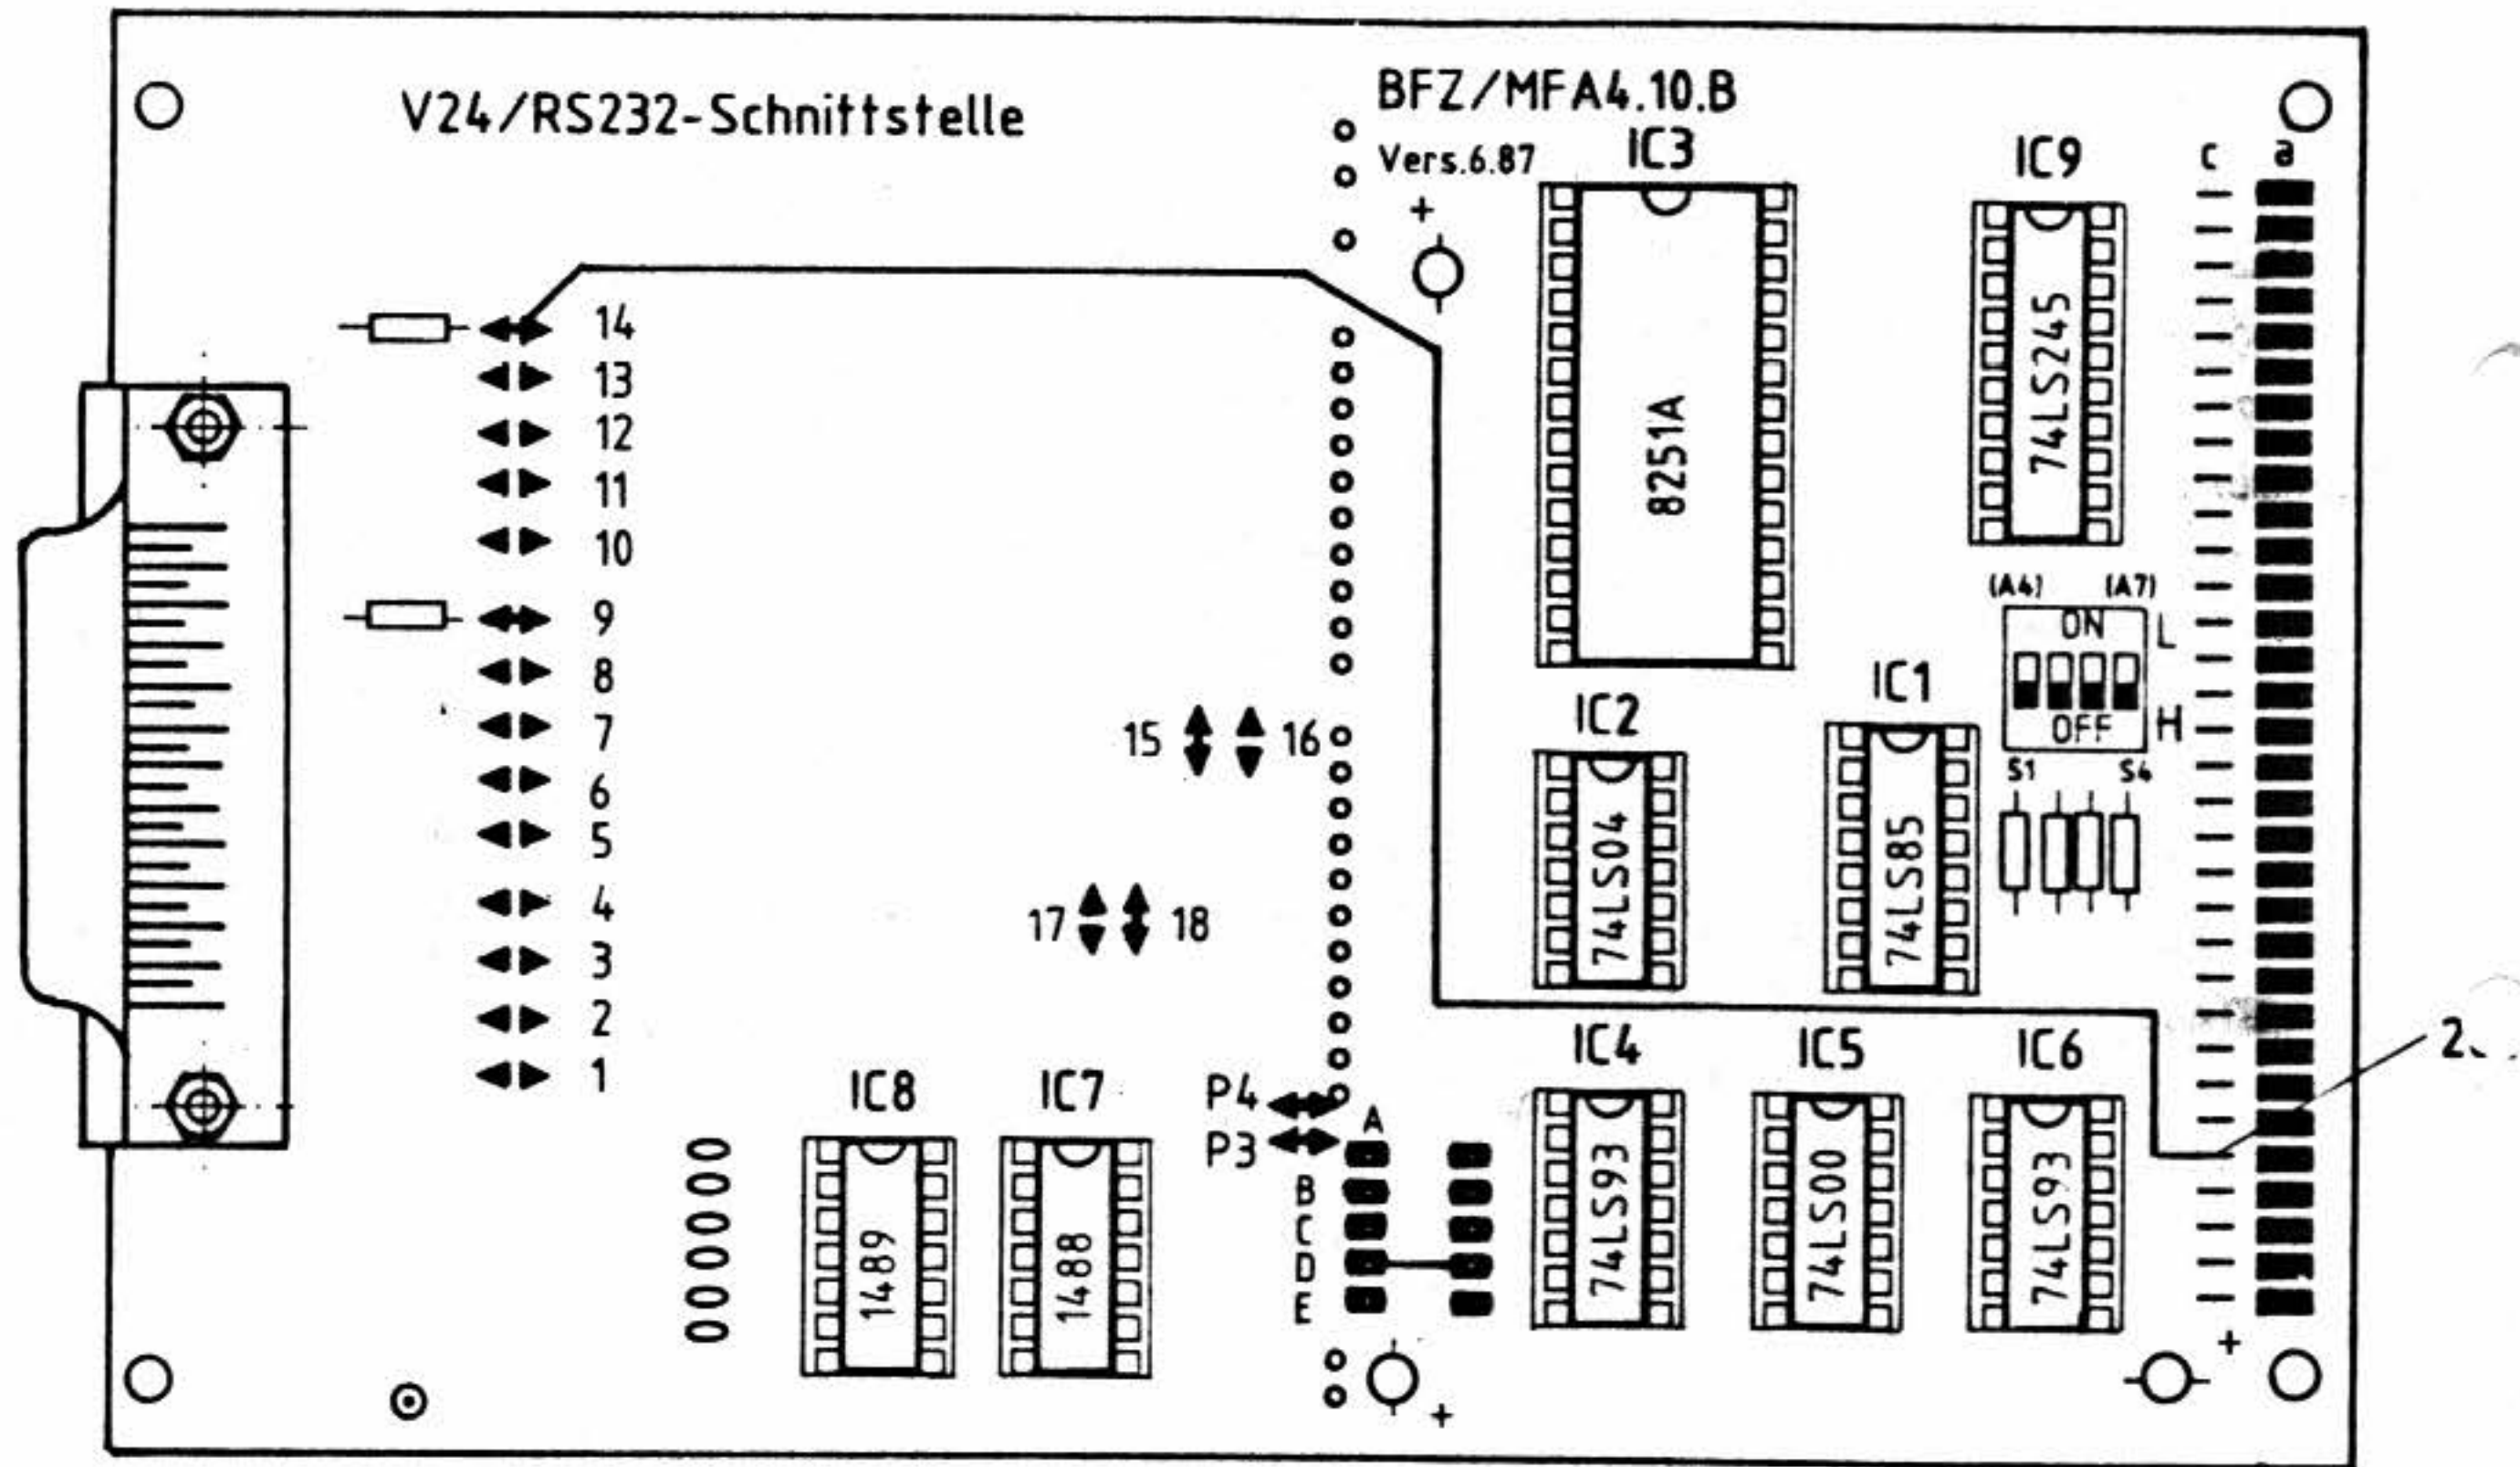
Bestückungsplan der V24/RS232-Schnittstelle
